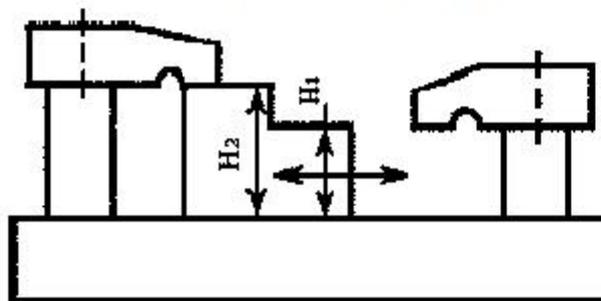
Приспособление с жесткими предельными элементами.
